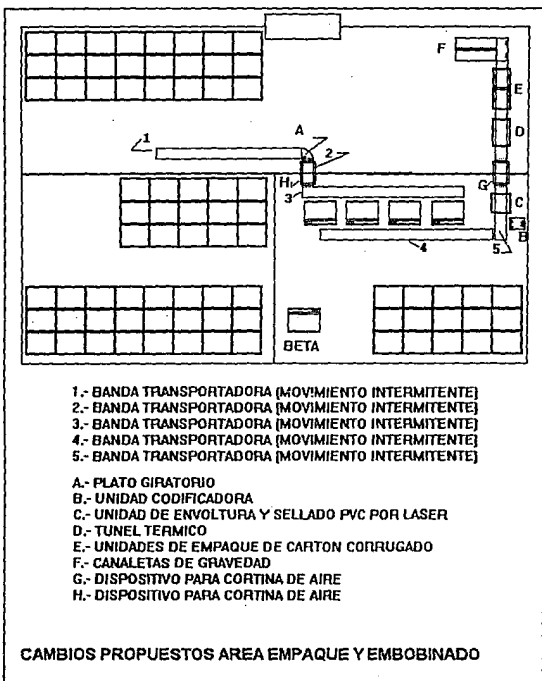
DIAGRAMA DE PLANTA PROPUESTO
